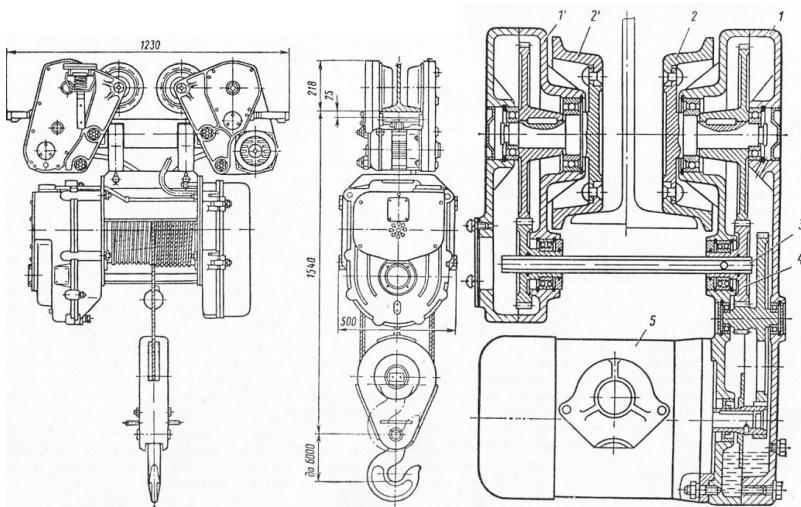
Устройство электрической тали: 1 – корпус; 2 – опорные колеса; 3 – соединительный вал; 4 – сателлитная шестерня второй ступени передачи привода; 5 – электродвигатель привода перемещения тали
